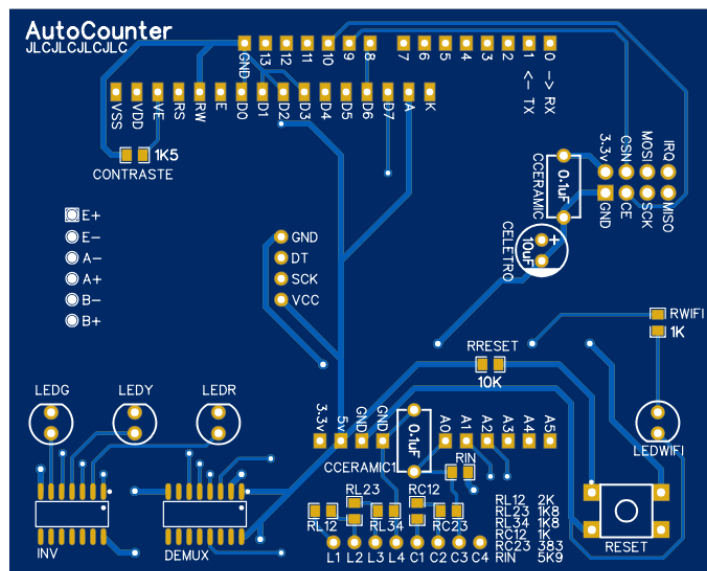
Vista frontal da PCB. Fonte: Elaborada pelo autor.
